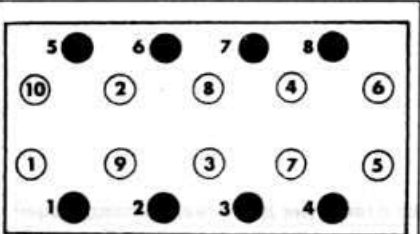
Порядок отворачивания болтов крепления головок цилиндров
